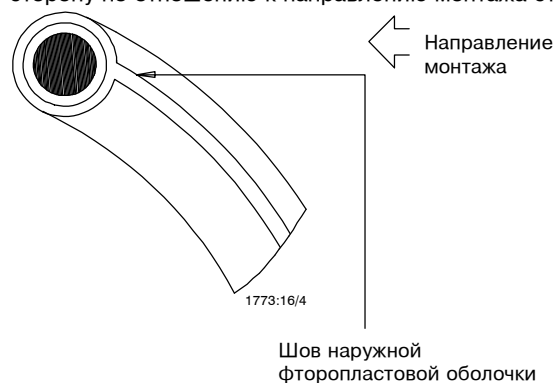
Прокладка круглого сечения с фторопластовой оболочкой
